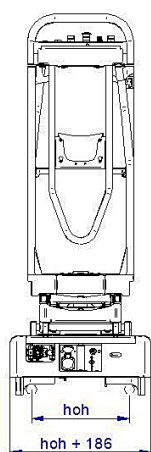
; Dimensions de la largeur en mm, 3 pantographes
